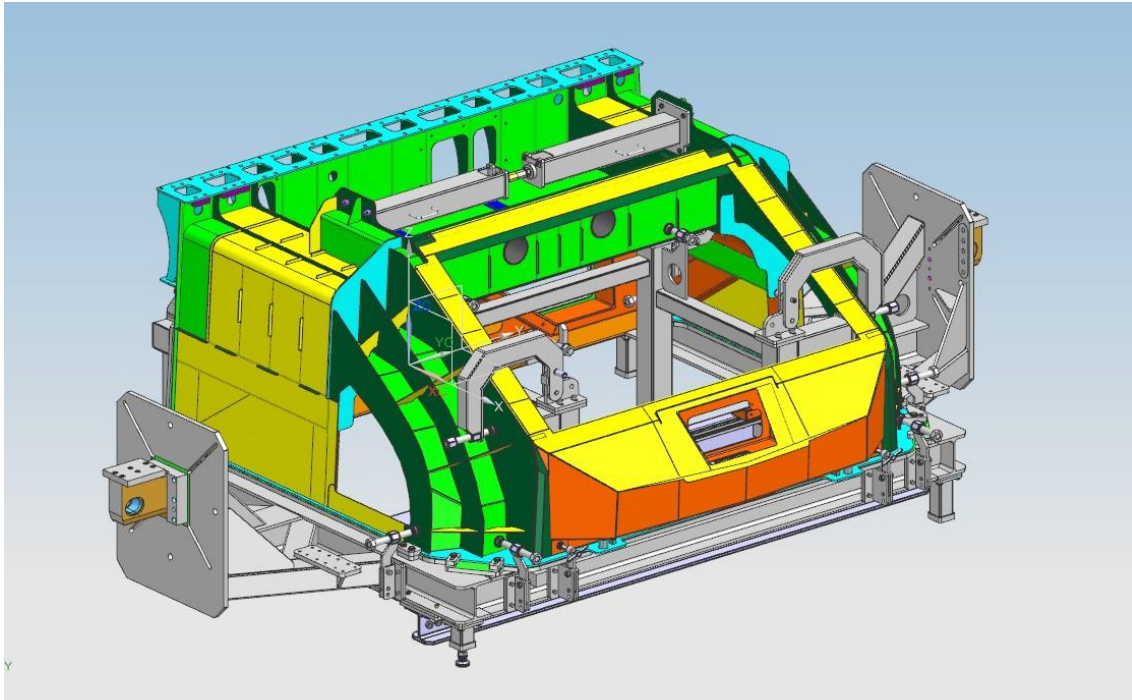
Útil U17053400S002100 – Montar Frontis 3 en 1.
